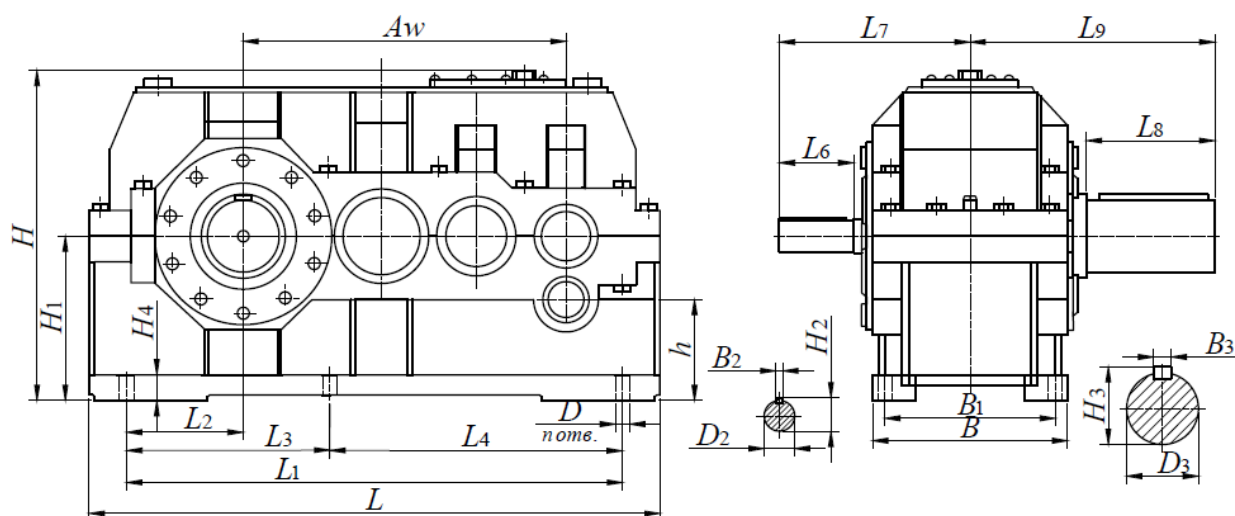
Редукторы цилиндрические четырехступенчатые
